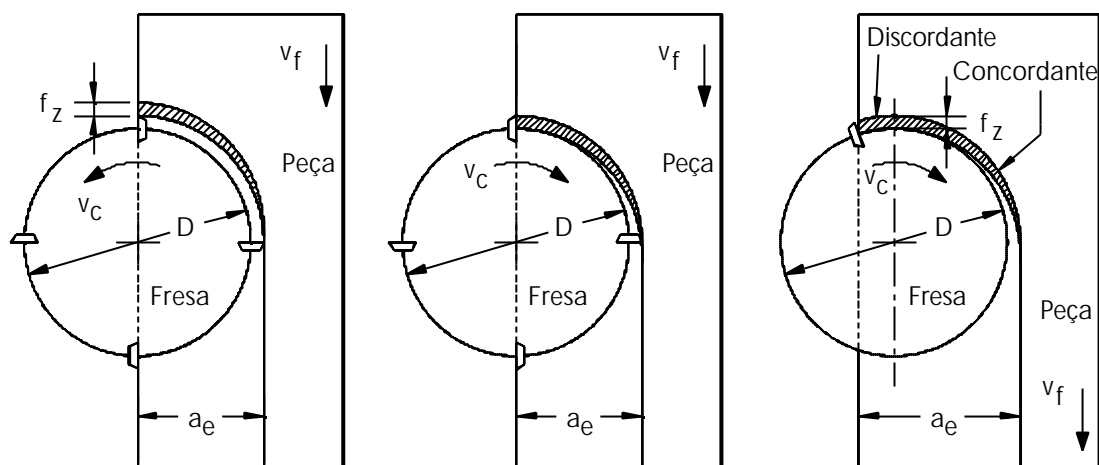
Fresamento discordante, concordante e combinado [20].
